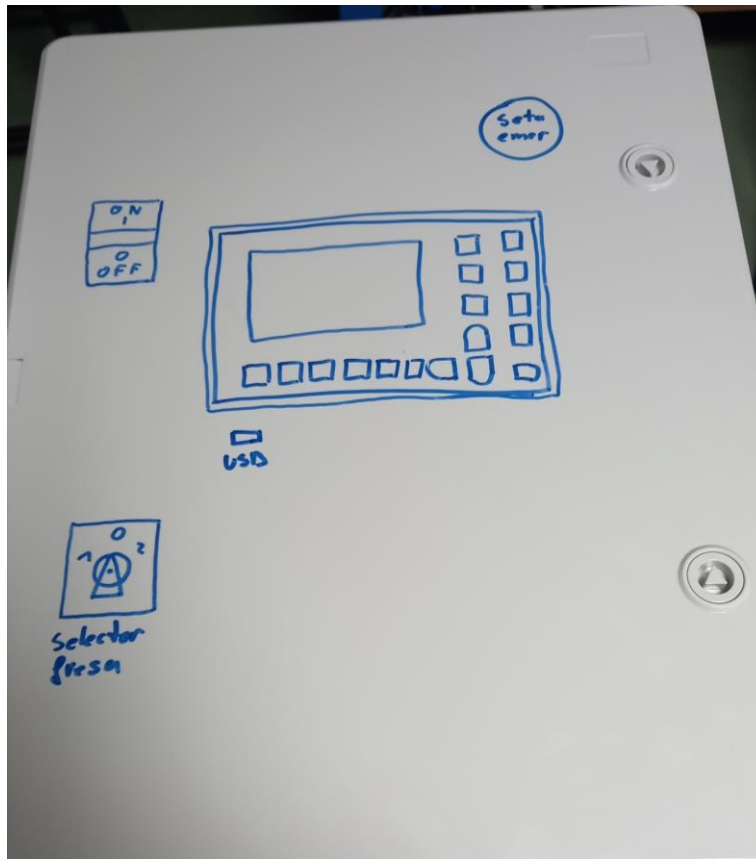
Diseño del panel frontal del controlador. (Elaboración propia)
